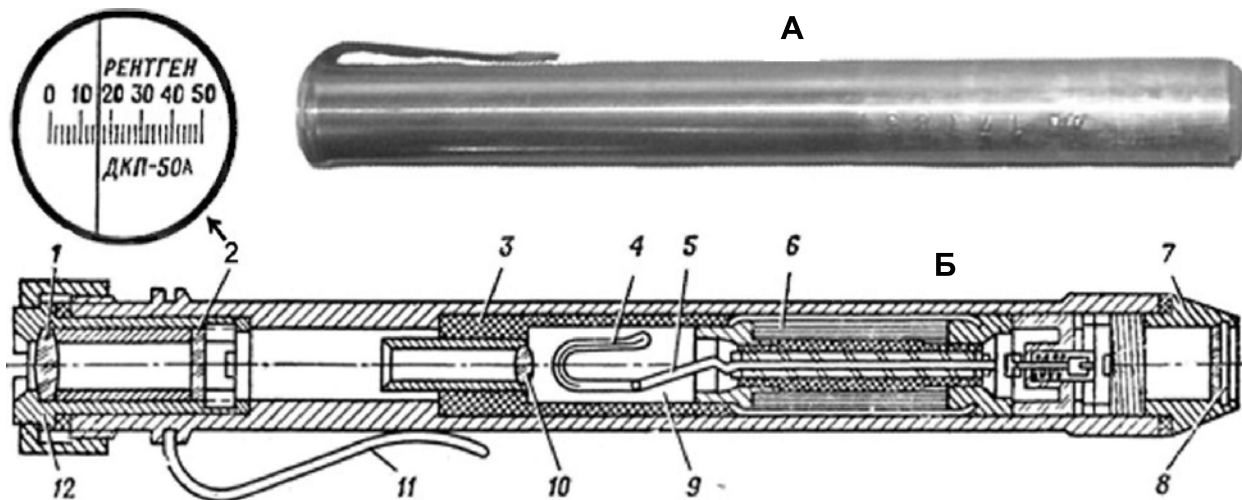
Измеритель дозы ДКП-50А: А) общий вид; Б) схема устройства
